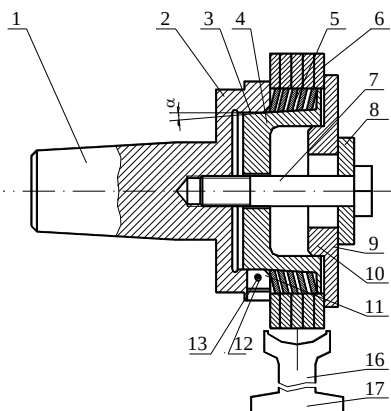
Оправа для профілювання гвинтових заготовок та процес проточування на верстаті
